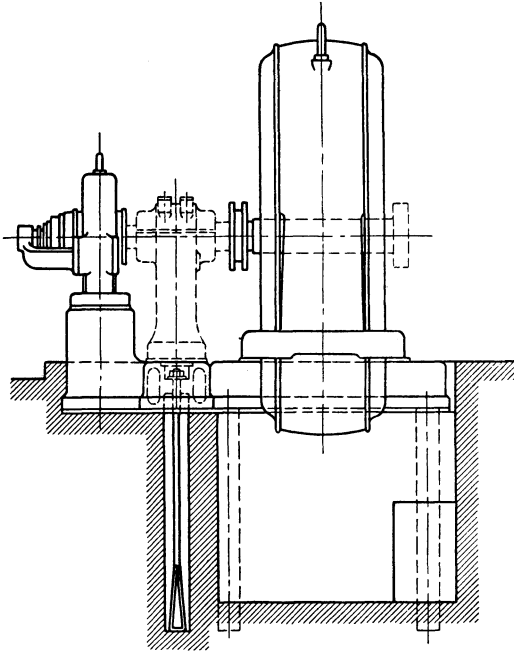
Drehstromgenerator mit Erregermaschine, Außenlager und Flanschelle für Zusammenbau mit Kolbendampfmaschine.
